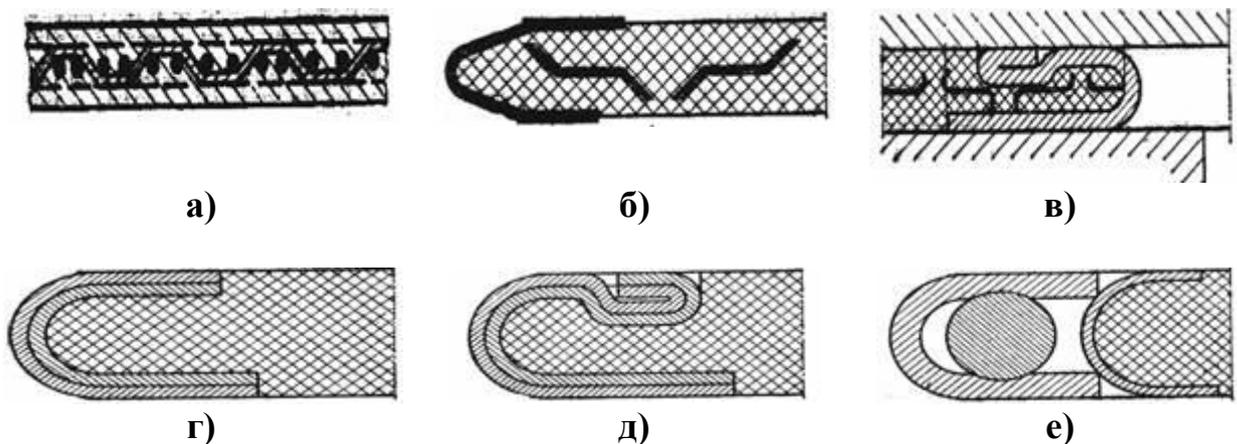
Прокладки для уплотнения газового стыка двигателей
